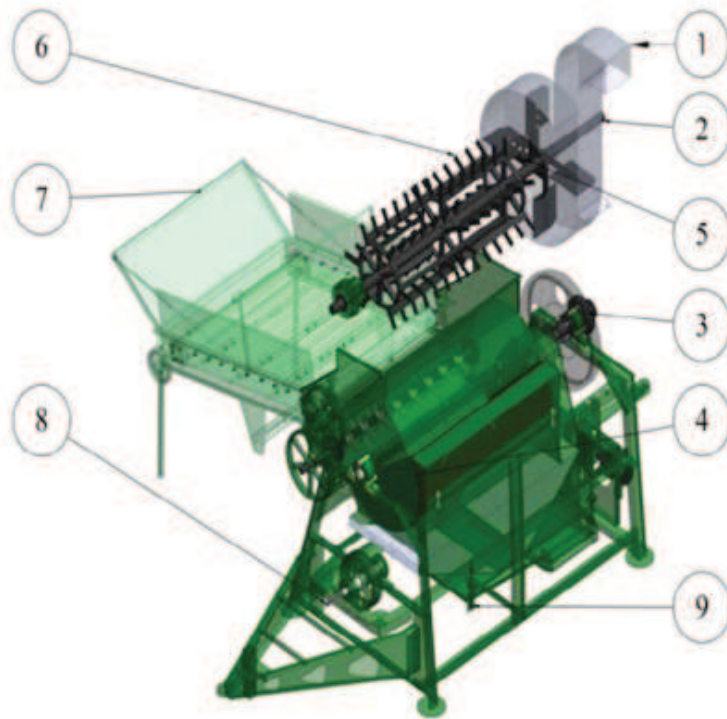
Vista explosionada de máquina trilladora con cilindro de dientes
